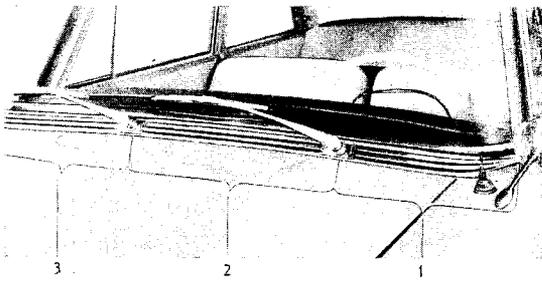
Zierleiste für Windlaufverkleidung eingebaut
